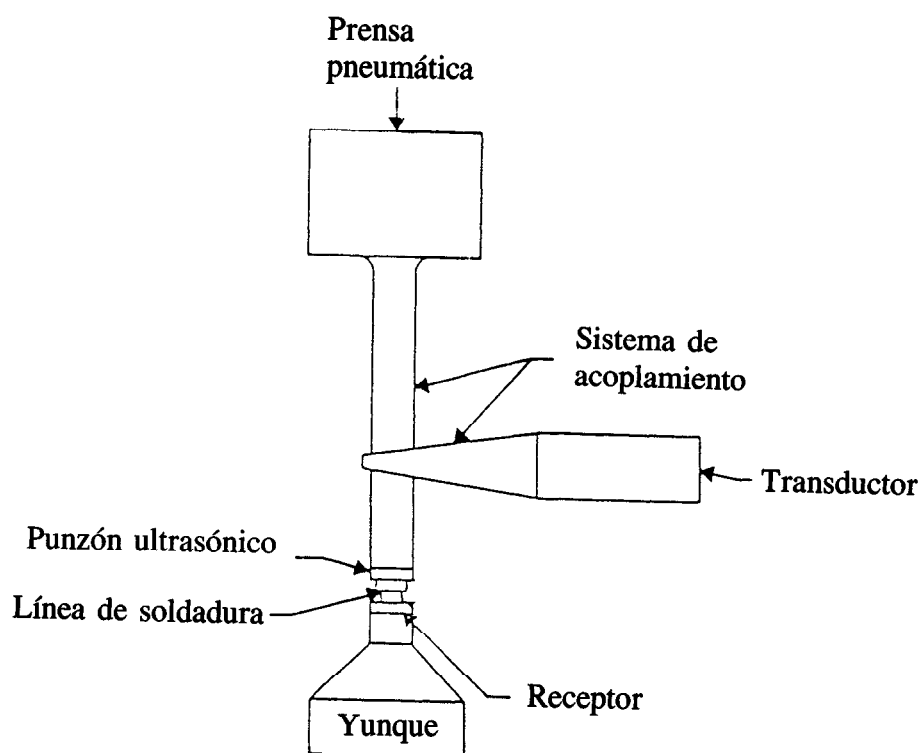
Elementos de la soldadura ultrasónica.
